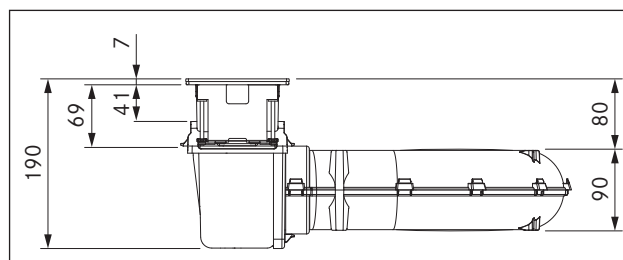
CKA2 dimensioni apparecchio vista frontale
